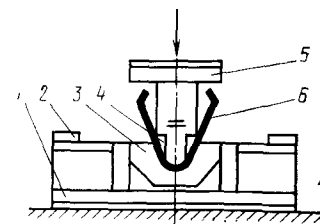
Схема штамповки обечайки направляющего ролика
